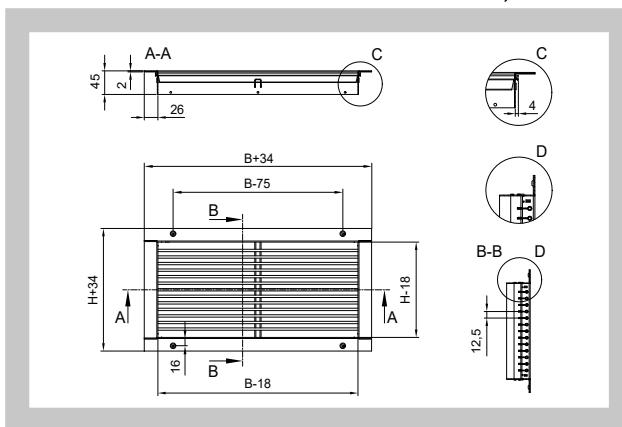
Feste Lamellen - Lamellenabstand 12,5 mm B > 600 mm
